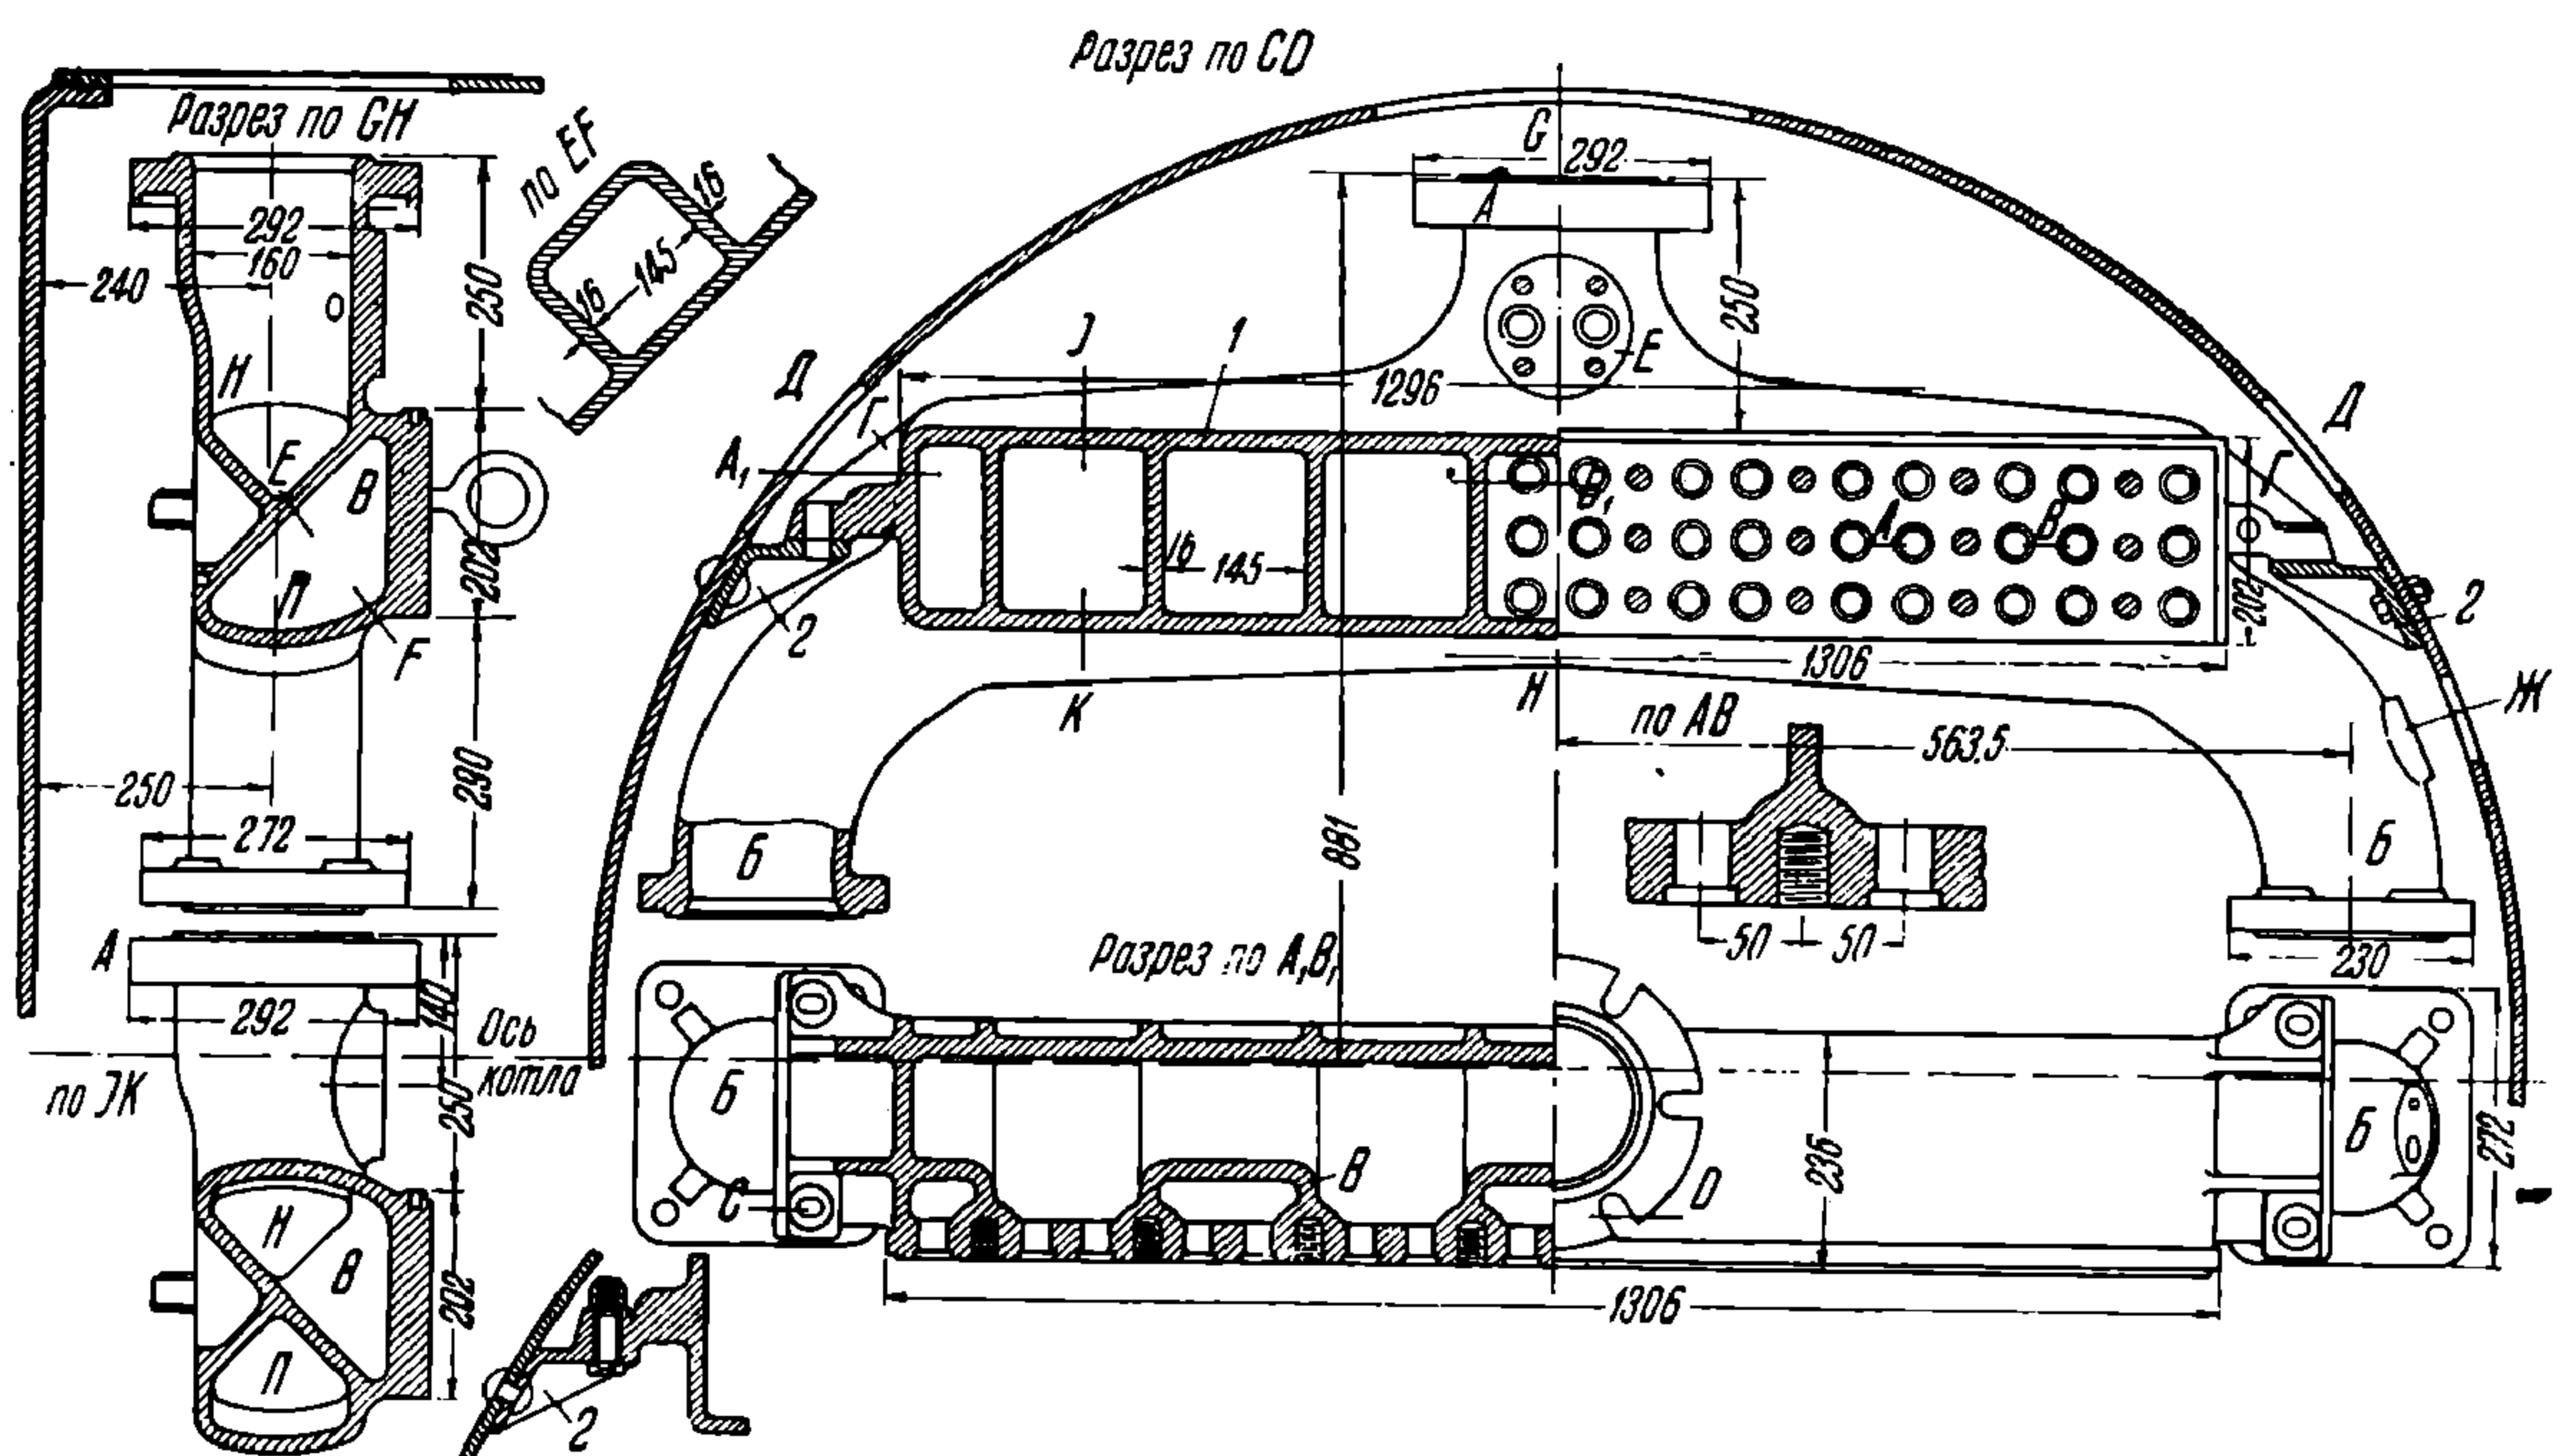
а. Подвески камеры пароперегревателя в дымовой коробке паровоза 2—3—0 Б.
